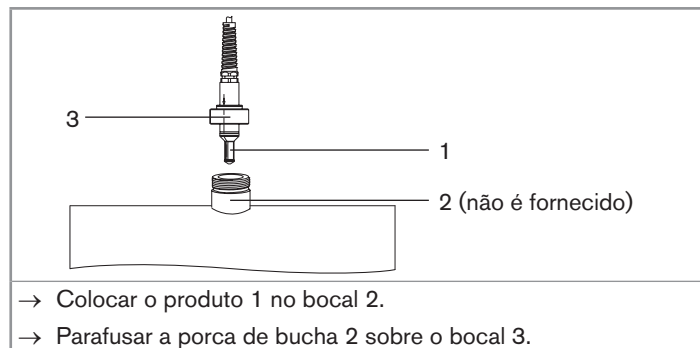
Instalação de um 8221 com conexão G1 1/4" em um tanque
